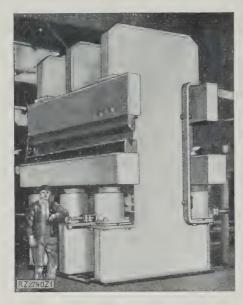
Hydraulische Presse für 1000 t Druck, ausgeführt als elektrisch geschweißte Stahlkonstruktion.
